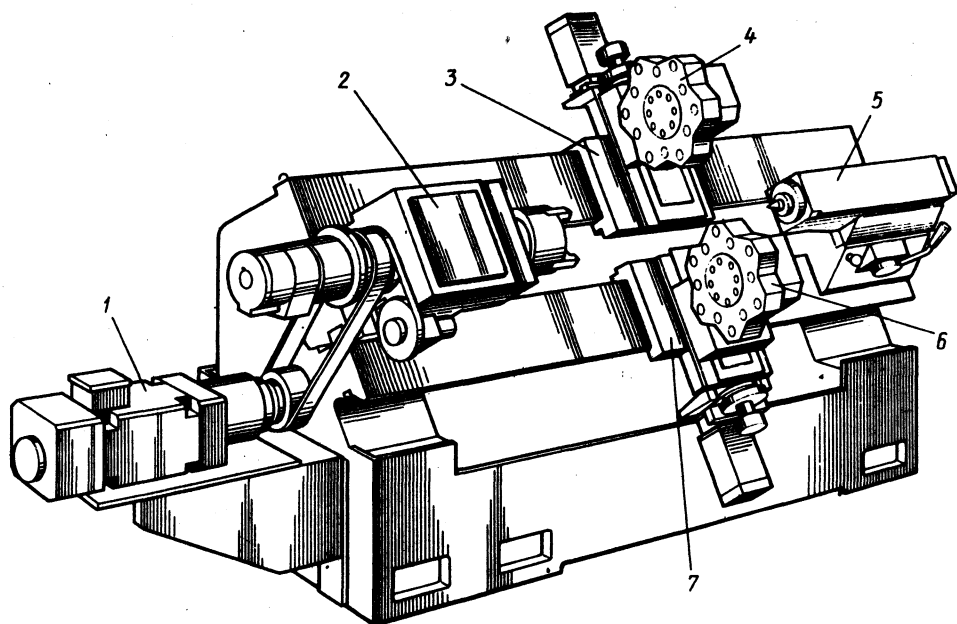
Компонка токарного станка с ЧПУ с наклонным расположением суппортов с двумя револьверными головками:
